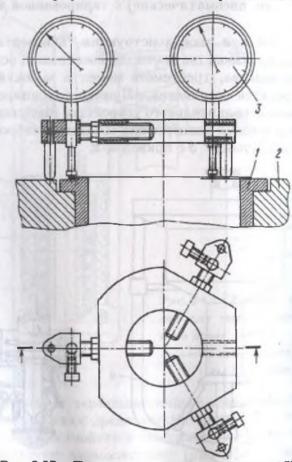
Приспособление для контроля положения гильзы цилиндра:
